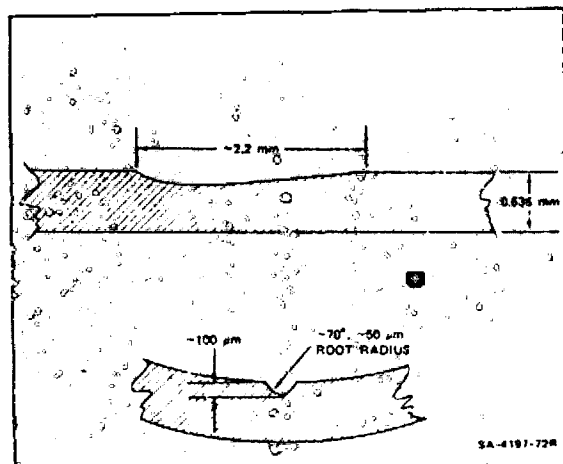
Forma y dimensiones reales de un típico defecto maquinado (Ref. 17).
